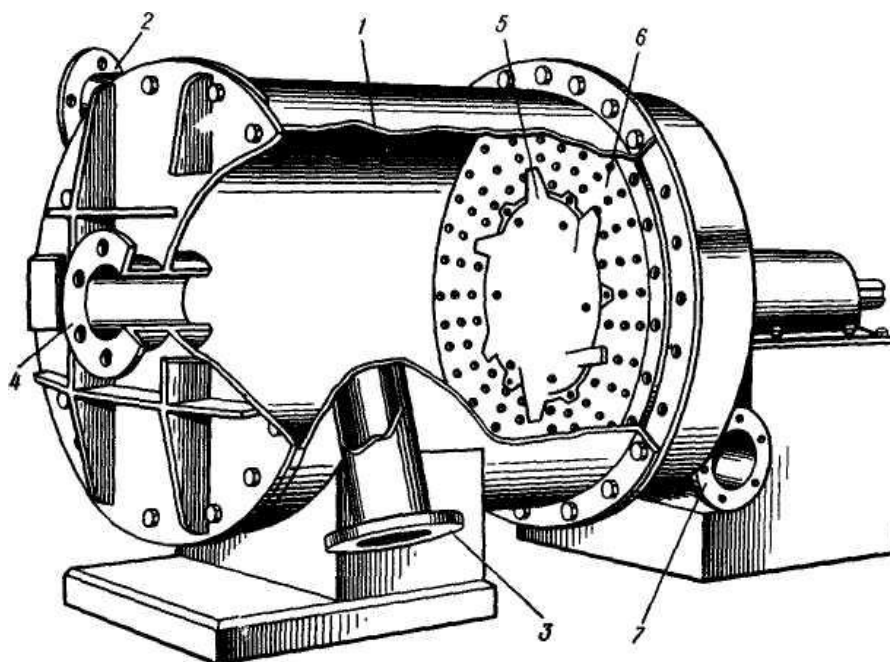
Сортирующий гидроразбиватель Белкор: 1 - ванна; 2 — патрубок подачи массы; 3 — патрубок отвода тяжелых отходов; 4 — патрубок отвода легких отходов; 5 — ротор; 6 — сито; 7 — патрубок отвода готовой массы
